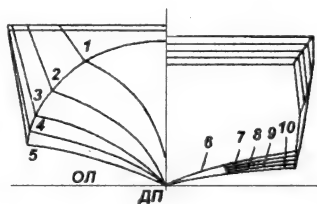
Теоретический корпус мотолодки «Казанка-2М»
